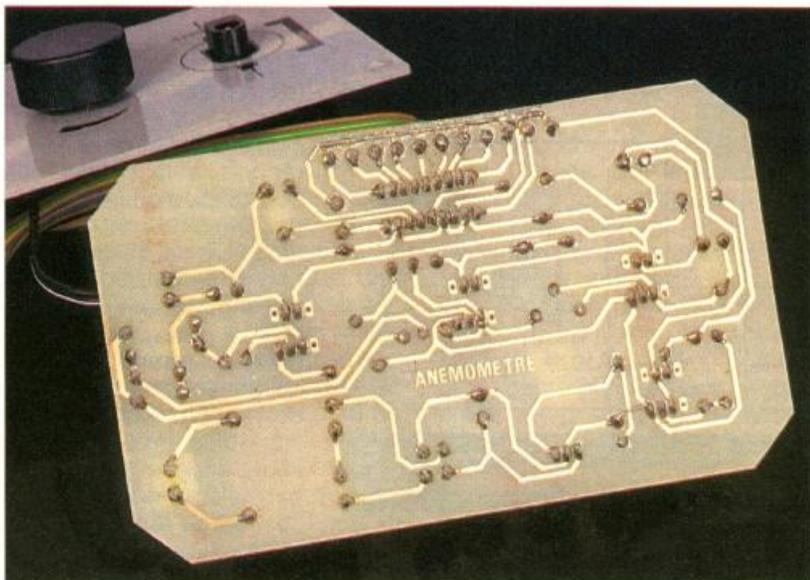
Vue du circuit imprimé côté soudures.
